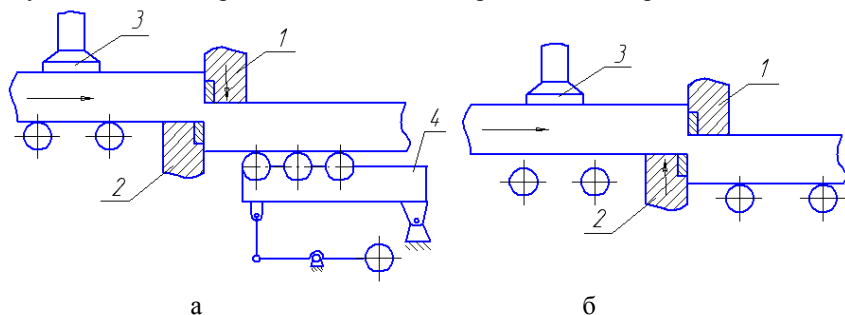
Схема резания металла на ножницах с верхним (а) и с нижним резом (б):
